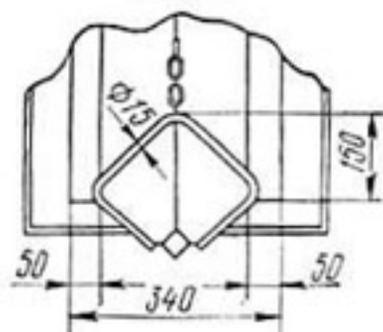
Конструкция сменного цельнометаллического сварного лотка к ЭТЦ-202А для укладки керамических труб с пластмассовыми соединительными муфтами:
